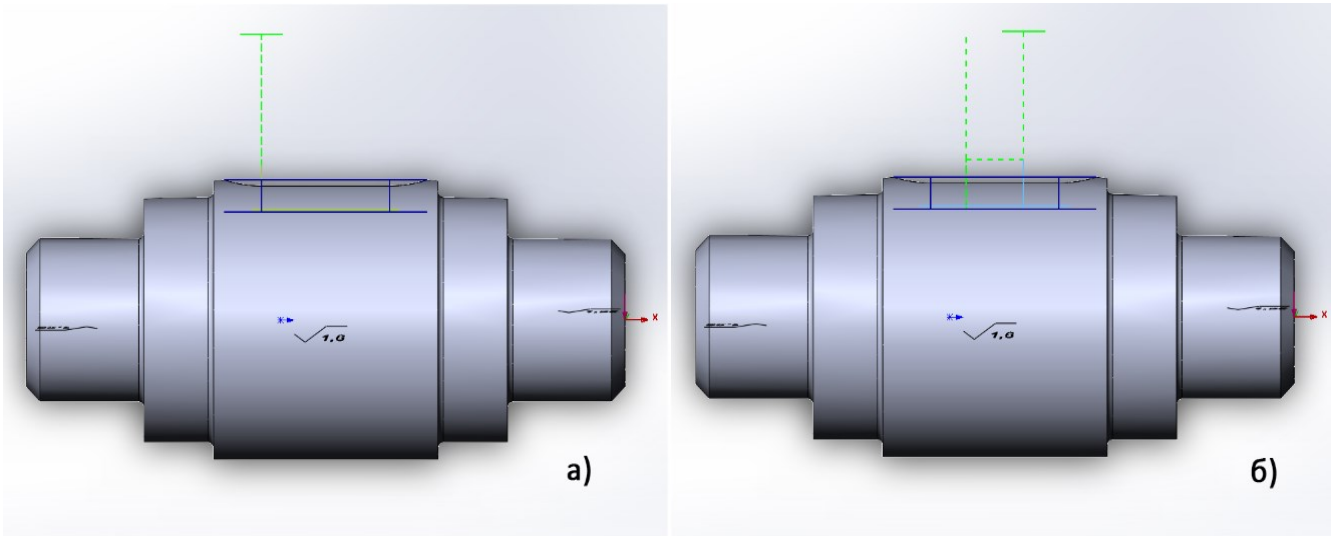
Траєкторія руху фрези: а) при свердлінні, б) при контурному фрезеруванні, Фрезерний установ.
